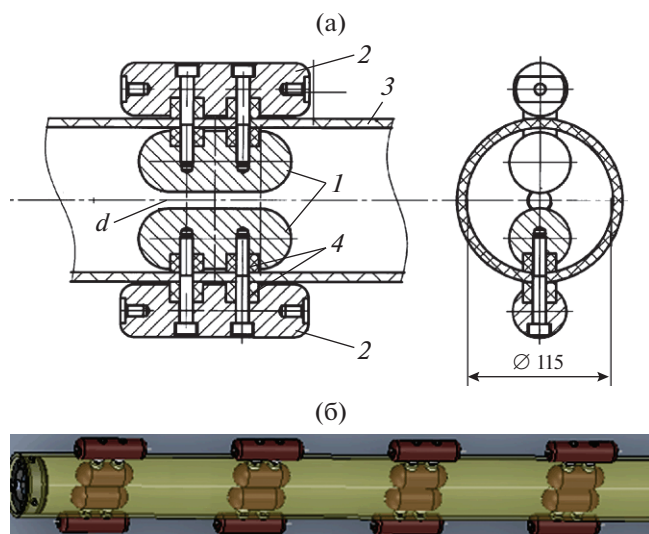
Сборка электродной системы разрядника (а). 1 – медные электроды; 2 – контакты для соединения с конденсаторами; 3 – корпус; 4 – уплотнительные кольца, d – искровой зазор; б – трехмерный вид.
